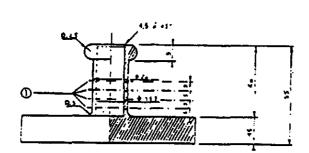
Cylindre creux en bronze, ferme d'un côte; plan et coupe verticale
